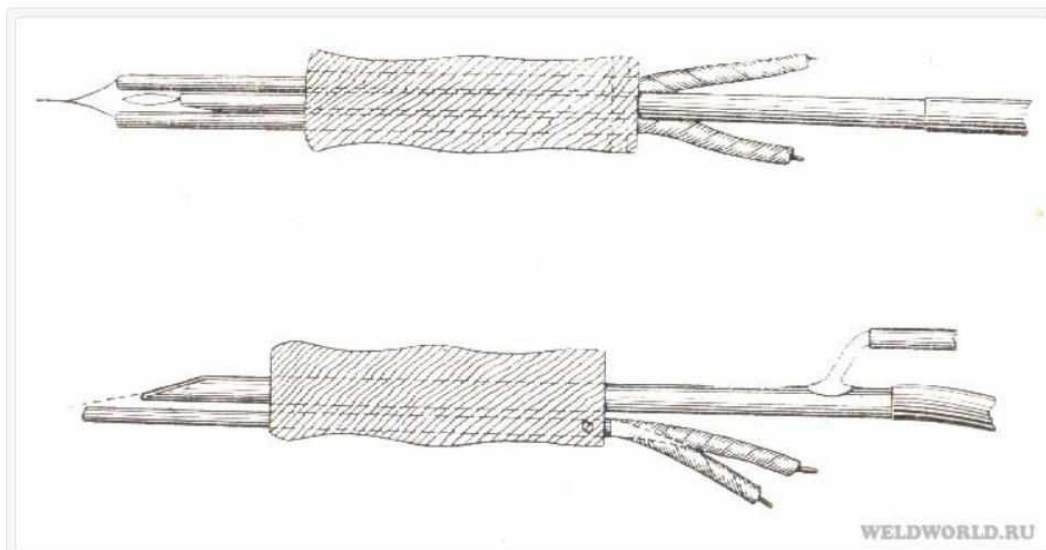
Suporte para soldagem a arco independente em atmosfera blindada – Weldworld.ru
